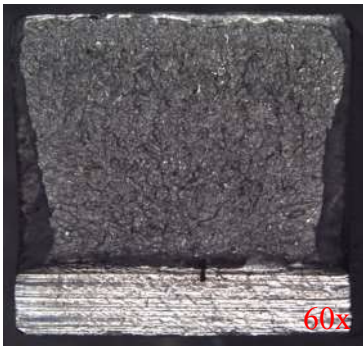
Vista macroscópica de la fractura 22MnB5, -35°C, condición 2.
